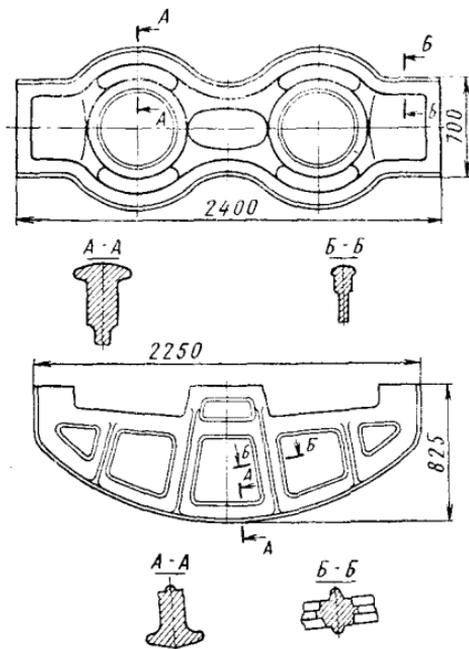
Крупногабаритные поковки из алюминиевых сплавов
